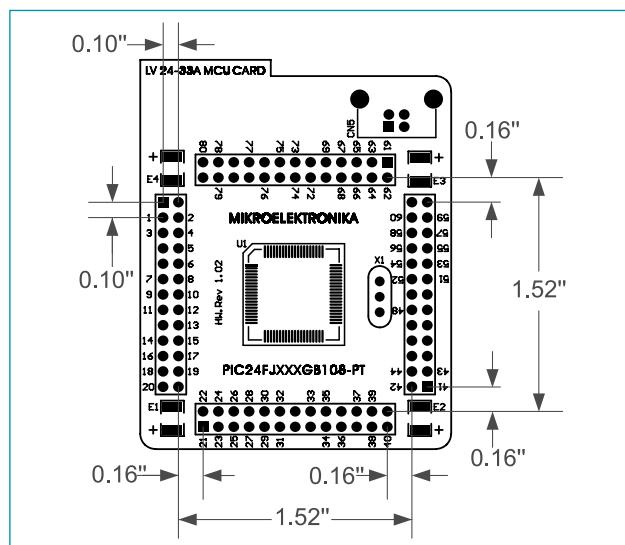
Dimensiones de la tarjeta MCU para la *MCU Card 13
